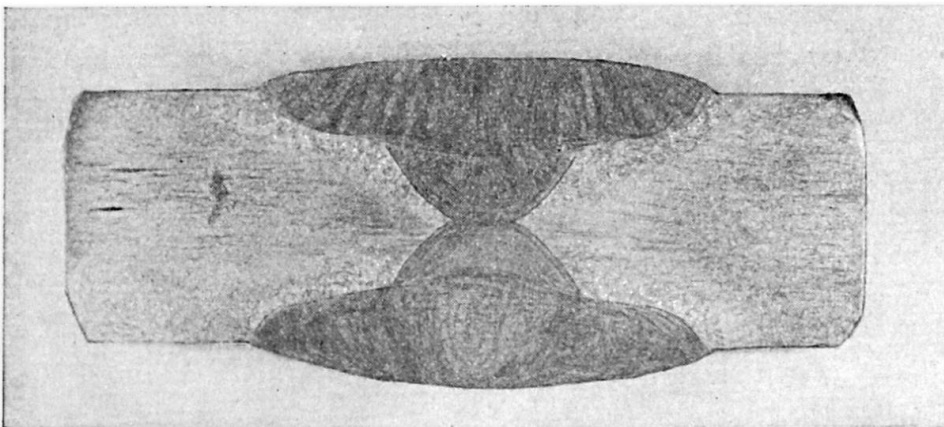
Makroschliff einer I-Schweissnaht in einem 16 mm Blech, mit OK Rapid geschweisst.
